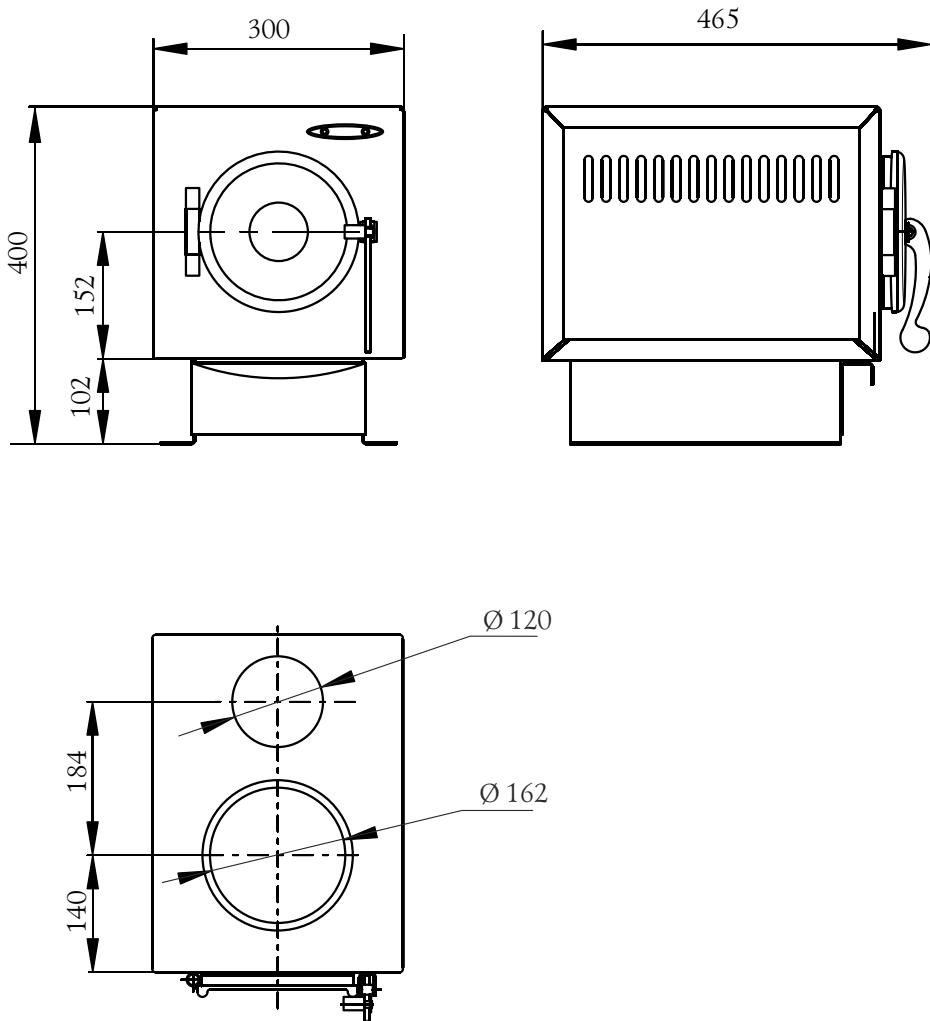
Габаритные размеры печи «Золушка 2016».
